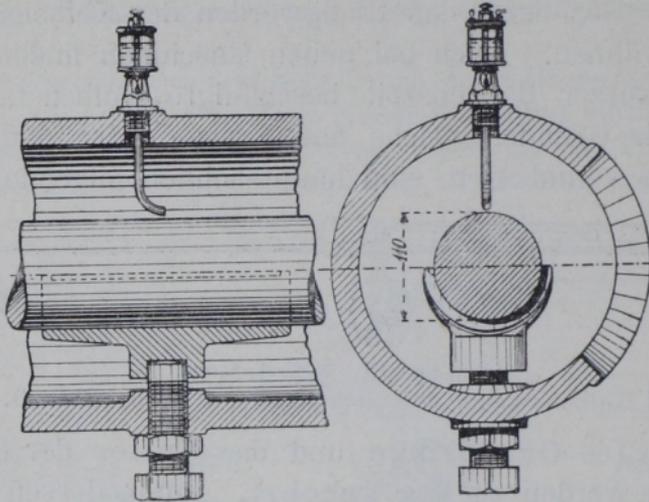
173. Schmierung der Kolbenstange für Tandemaschinen im Verbindungsstück der beiden Cylinder.
